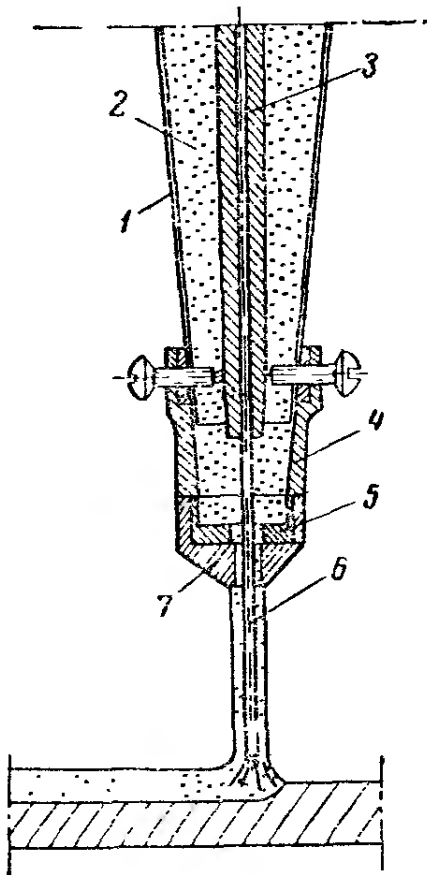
Схема процесса сварки с намагничивающимся флюсом
